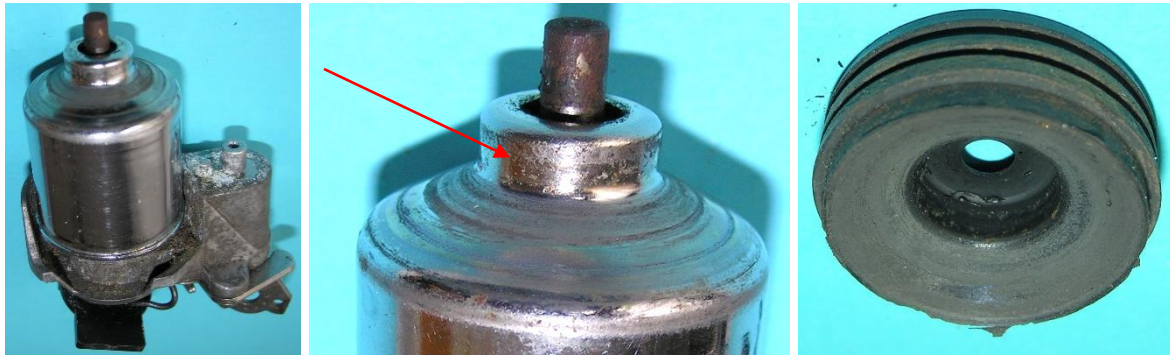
Laufringsitz: a) Dynamokörper mit Kippvorrichtung, b) Sitz des Laufrings über dem oberen Kugellager, c) Gummilaufing
